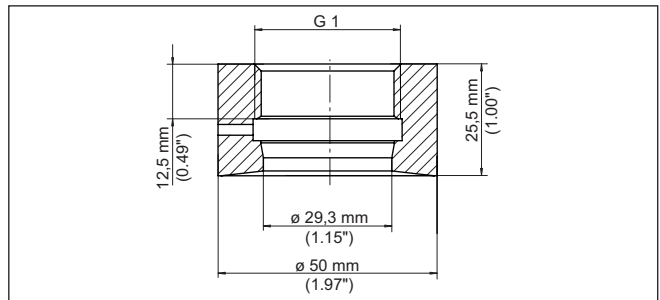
Maße Direkt-Einschweißstutzen G1 (ISO 228-1) - O-Ring-Dichtung
